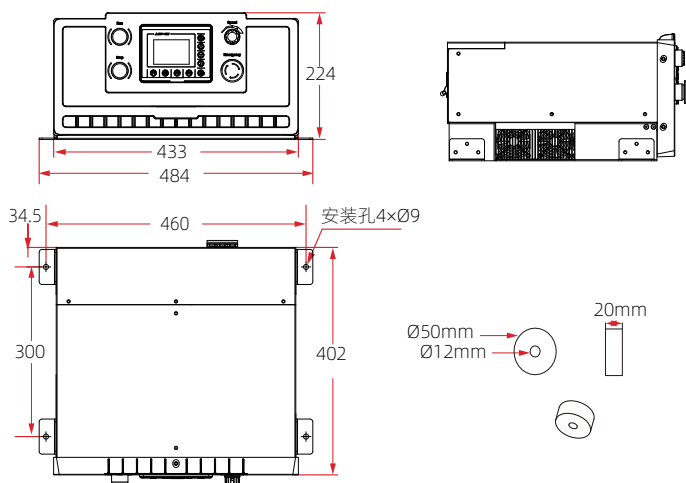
(一体风冷) 外型尺寸安装尺寸及减震垫示意图 (AWD100-4T0501~AWD100-4T1804) (单位: mm)
